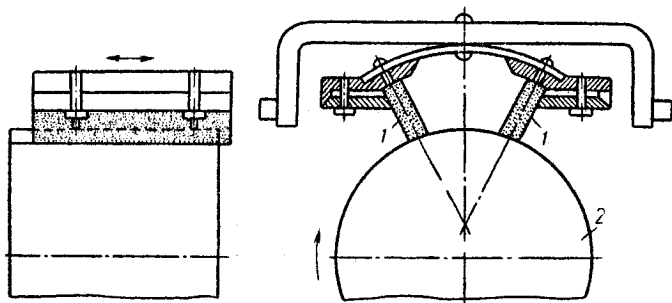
Схема суперфінішу поверхні деталі типу «вал»
